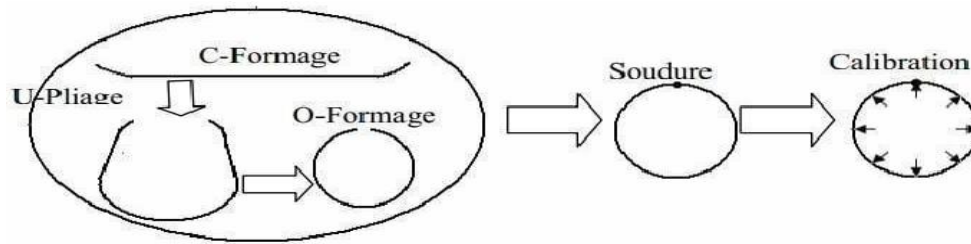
Les étapes de fabrication de pipes soudés le long du matériau (CTOA) [27].
